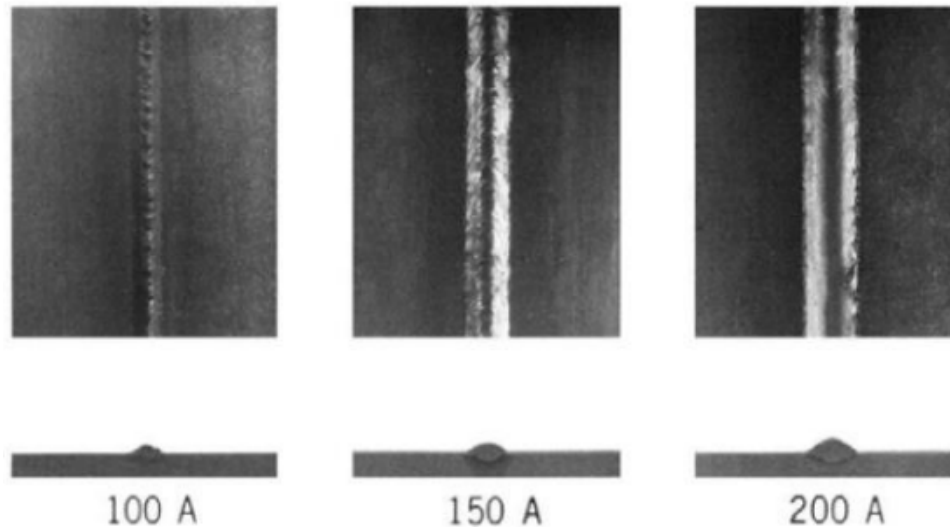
Efeito da corrente de soldadura na penetração da solda – aço carbono, curto-circuito, Ar-25%CO₂ [13].
